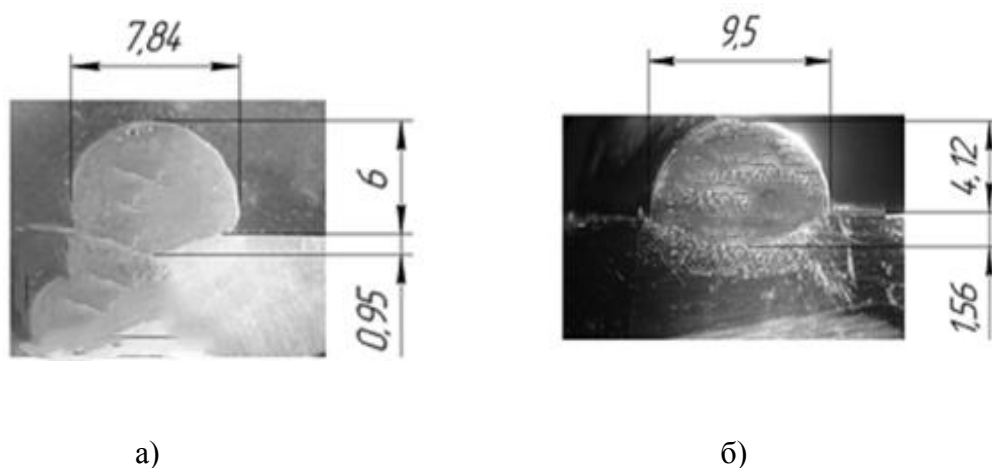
Геометричні параметри наплавленого валка: а) з вуглецевою тканиною;
